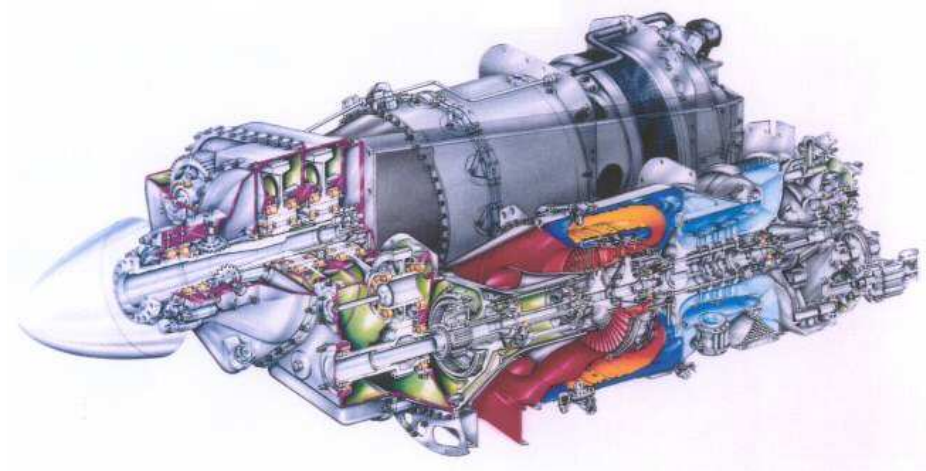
Zjednodušený obrázek motoru Soloy Turbine Pac (14)
